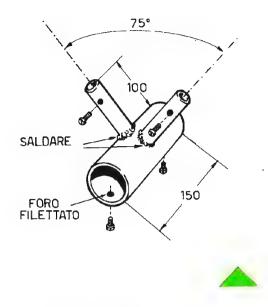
Giunto da applicare alle estremità dell'asta orizzontale tramite fissaggio a viti da ferro. Il diametro interno del tubo deve essere leggermente superiore al diametro esterno dell'asta orizzontale; questa stessa osservazione si estende ai due tubetti diagonali sui quali verranno innestate le asticelle.
